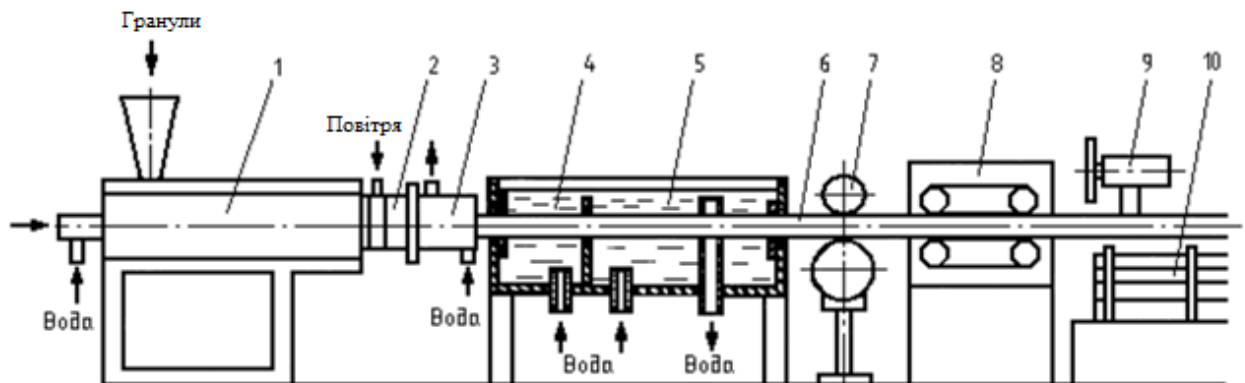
Схема агрегату для виробництва труб методом екструзії, де 1 - екструдер; 2 - формуюча головка; 3 - калібруюча насадка; 4, 5 - перша і друга зони охолодження; 6 - трубчастий профіль; 7 - вимірально маркуючий пристрій; 8 - тягучий пристрій; 9 - відрізаючий пристрій; 10 - приймальний стіл (штабелювальний пристрій).
